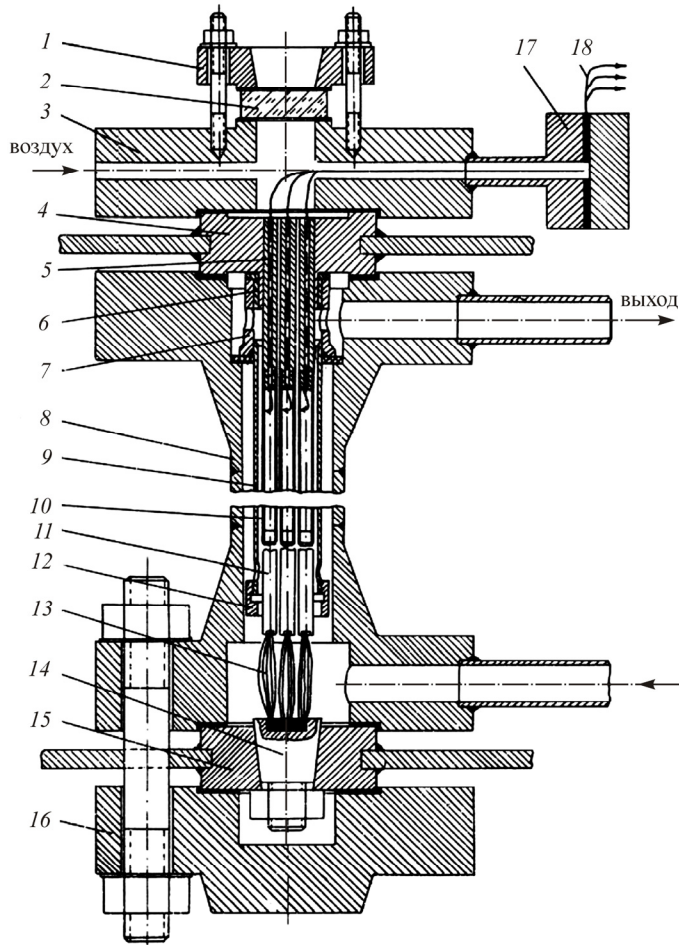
Корпус канала ТВС, имитирующей корпус натурной установки: 1 – фланец для уплотнения смотрового стекла; 2 – смотровое стекло; 3 – верхняя крышка корпуса; 4 – верхний токоподводный фланец; 5 – верхние полые токовводы; 6 – установочное кольцо; 7 – центрирующий стакан; 8 – корпус высокого давления; 9 – шестигранный канал; 10 – трубки пучка; 11 – нижние сплошные токовводы; 12 – фиксирующее кольцо; 13 – гибкие пластины; 14 – контактный конус; 15 – нижний токоподводный фланец; 16 – нижняя крышка корпуса; 17 – фланец без вывода термодпар; 18 – термодпары для фиксации кризиса
